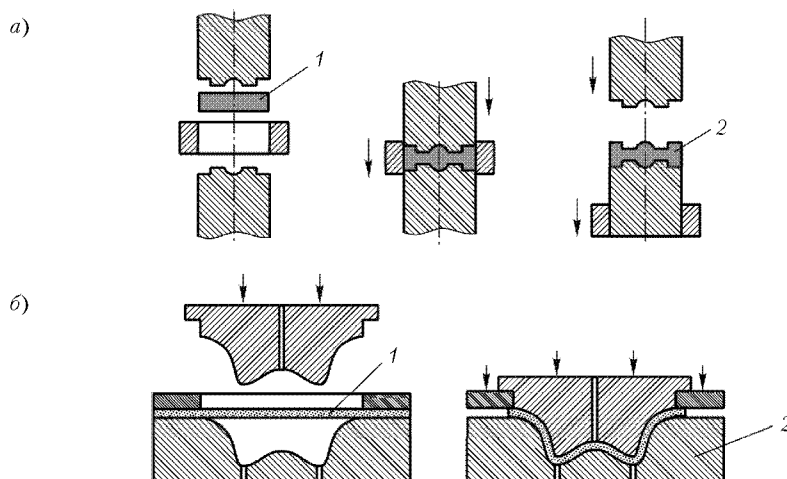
Формование изделий методом штамповки: а — объемная штамповка; б — плоская штамповка; 1 — заготовка; 2 — изделие
